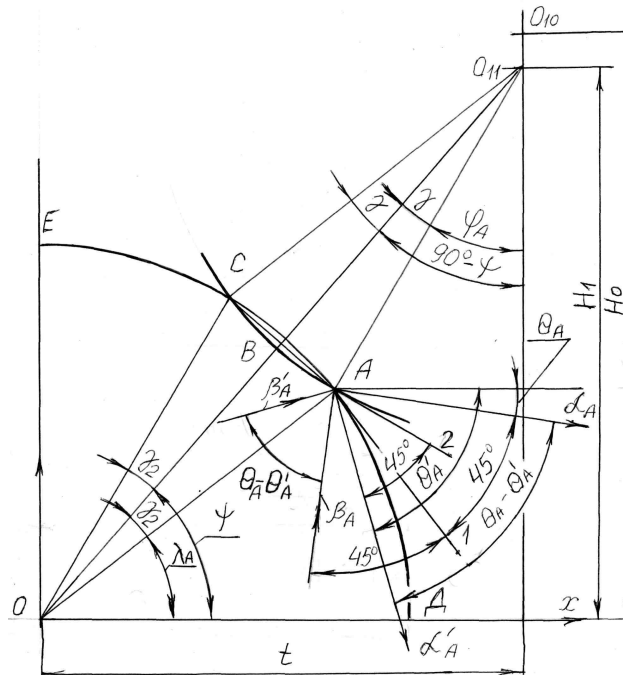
Схема процесса деформирования круглой заготовки на первой стадии
